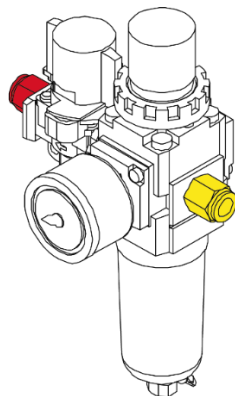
Монтаж пневматических разъемов на блок подготовки воздуха
